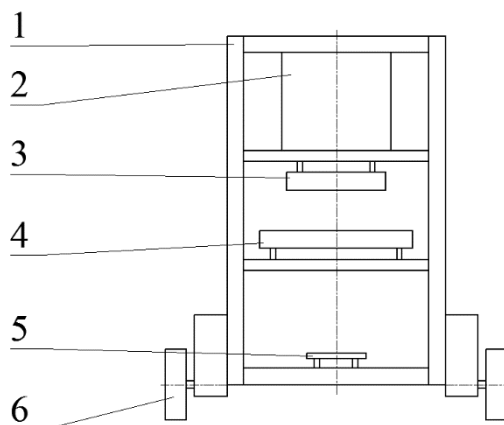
Концептуальная модель двухколесного робота: 1 – шасси робота; 2 – модуль питания; 3 – блок управления мотор-редукторами; 4 – блок микроконтроллера; 5 – акселерометр; 6 – мотор-редуктор с колесом
